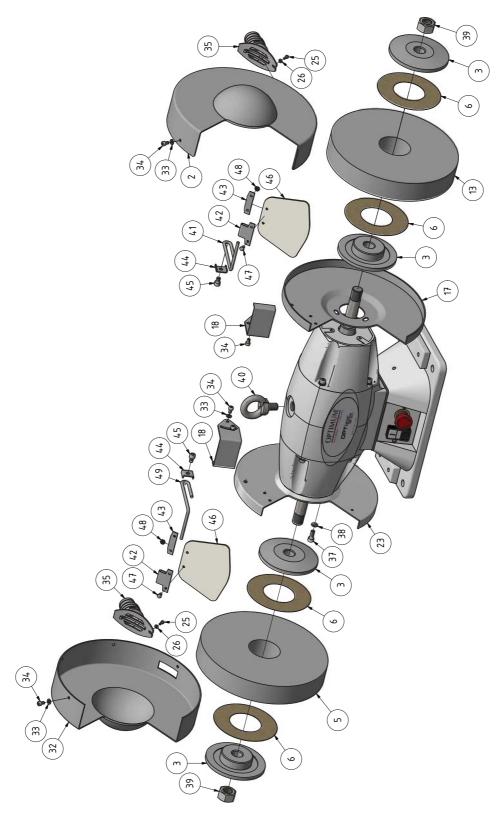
Ersatzteilzeichnung 1 von 2 - Drawing spare parts 1 of 2
